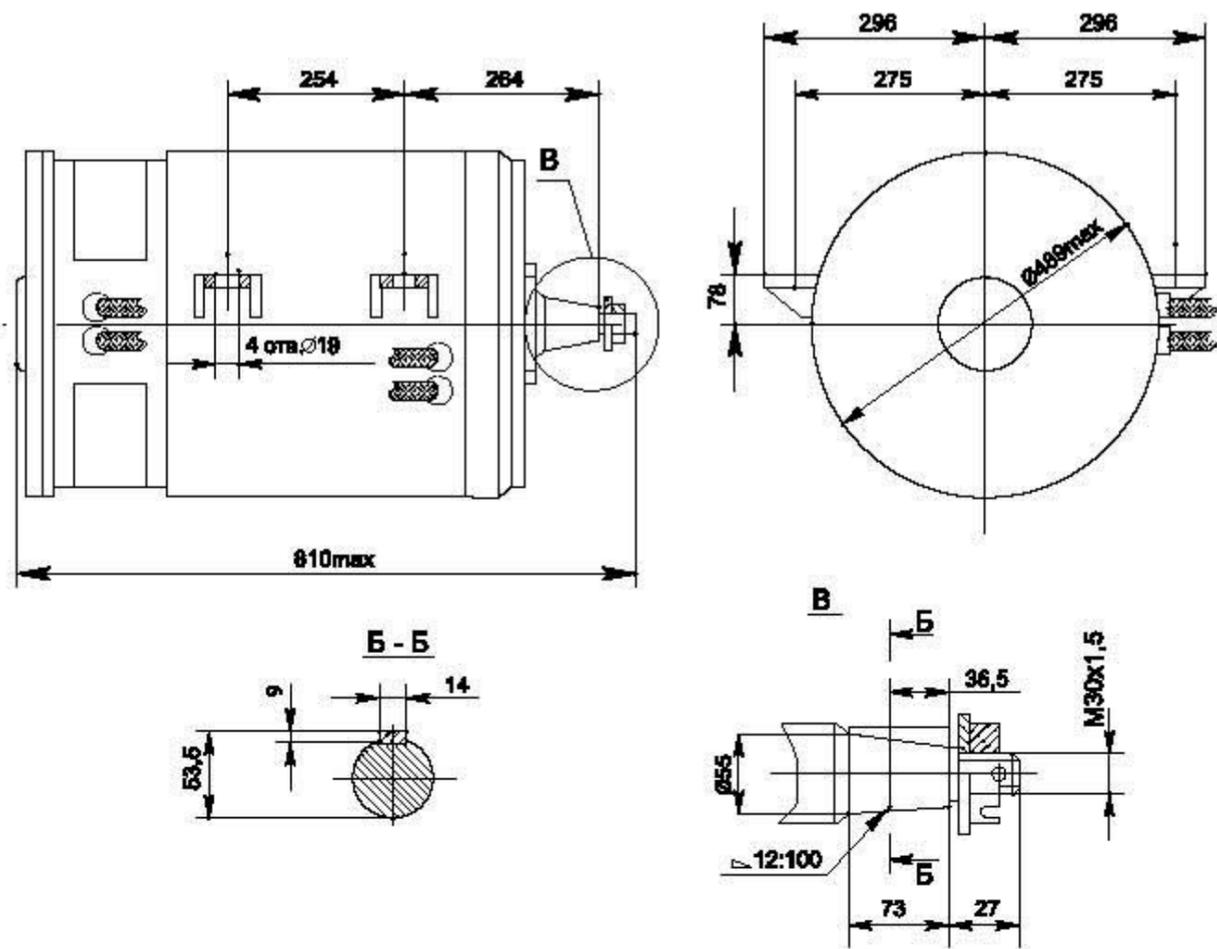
Габаритные, установочные, присоединительные размеры электродвигателей ДК-309М
